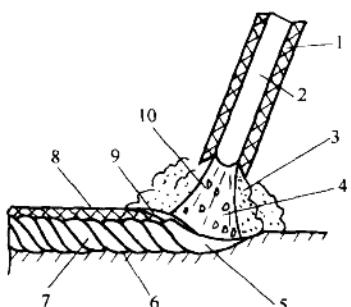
焊条电弧焊的焊接过程示意图
